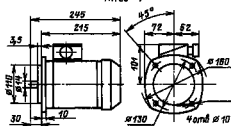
30 Габаритные и установочные размеры двигателя AA56-4, AA63-4
